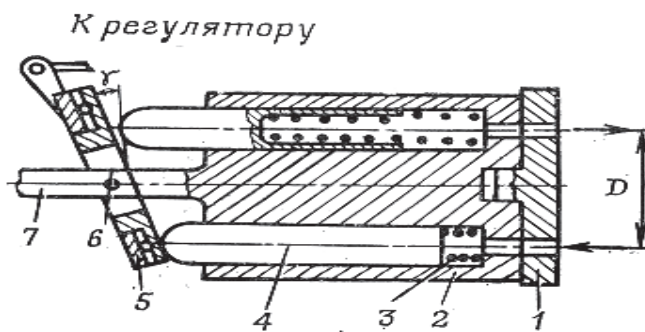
Схема плунжерного насоса: 1 – распределительный золотник; 2 – блок цилиндров; 3 – пружина; 4 – плунжер; 5 – наклонная шайба; 6 – ось; 7 – приводной вал
